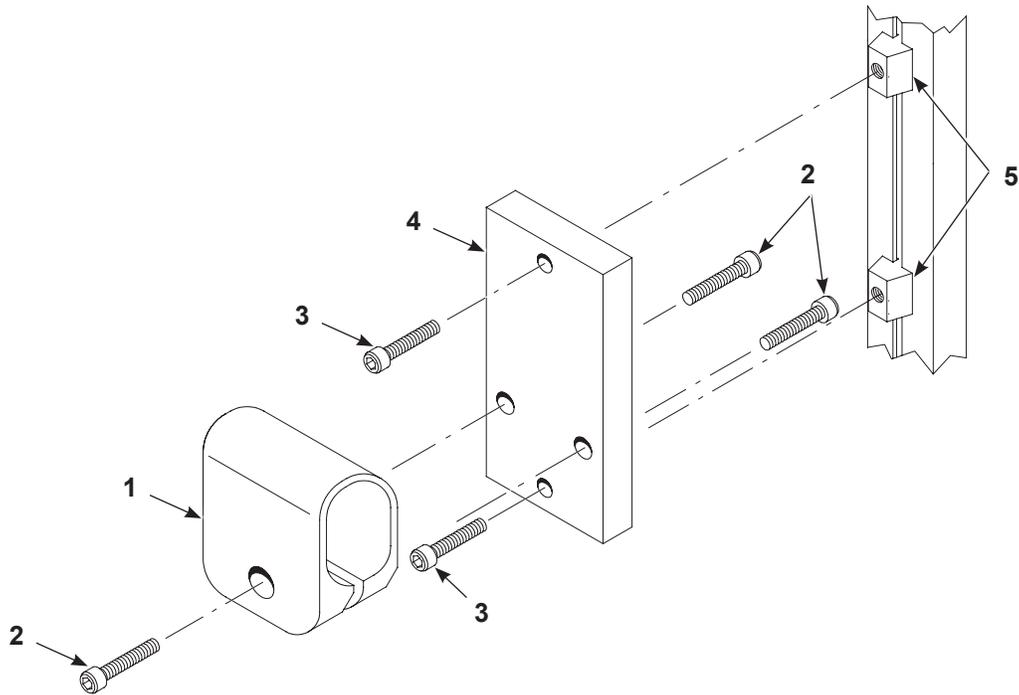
Conjunto de montaje de la pistola de aplicación de extrusión para pistolas de aplicación de montaje en tubo
